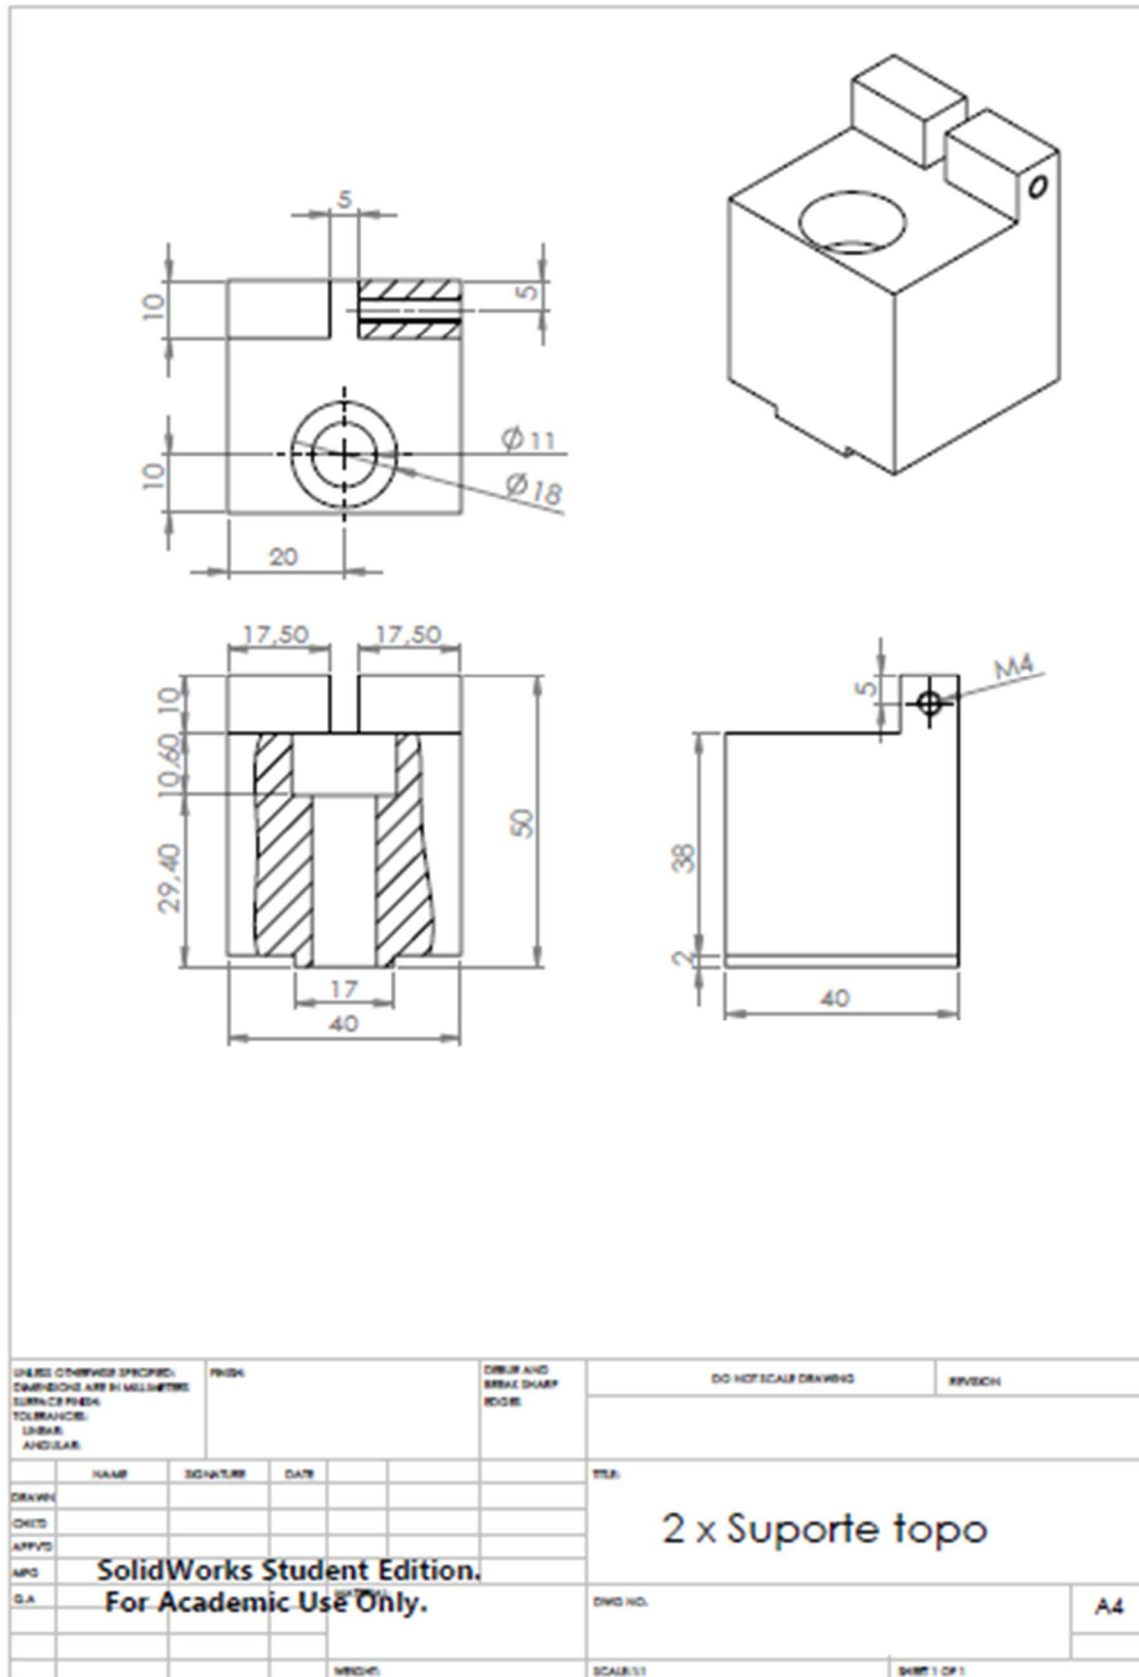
Desenho técnico do sistema de fixação longitudinal.
